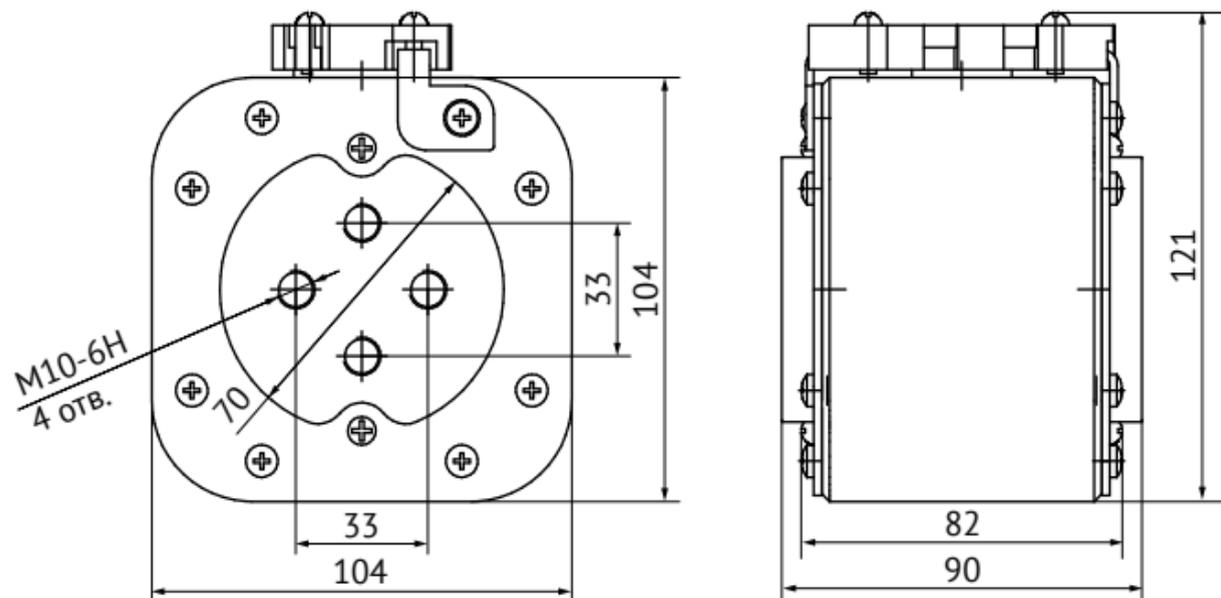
Размеры для OptiFuse FR-S84-1250V-(1000-2500)A
